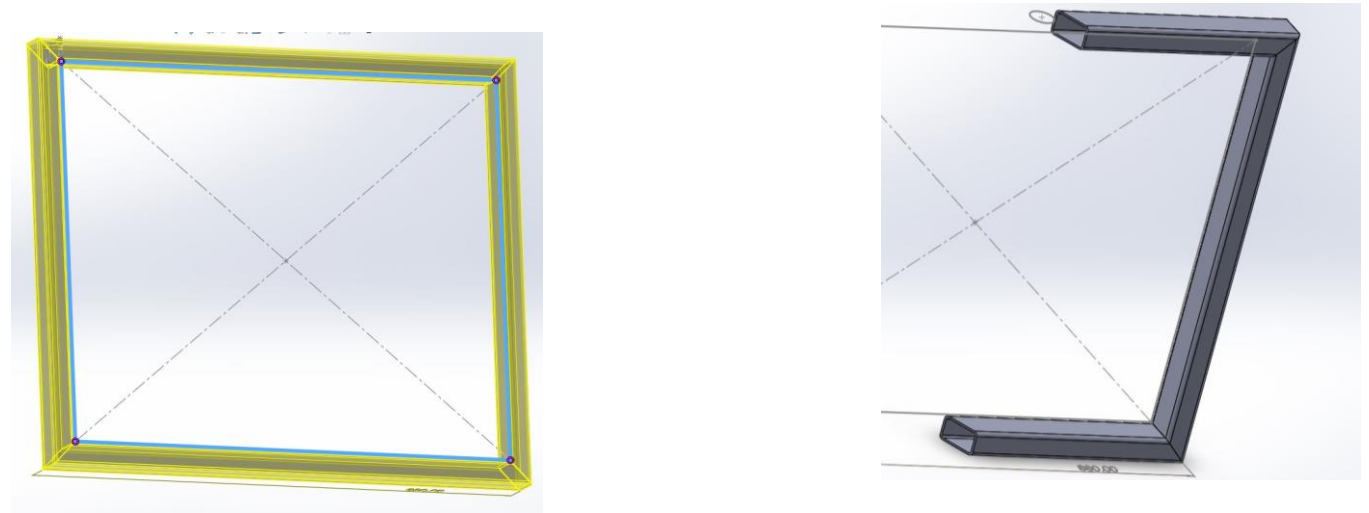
cadre 02 sous forme poutre et vue en coupe
